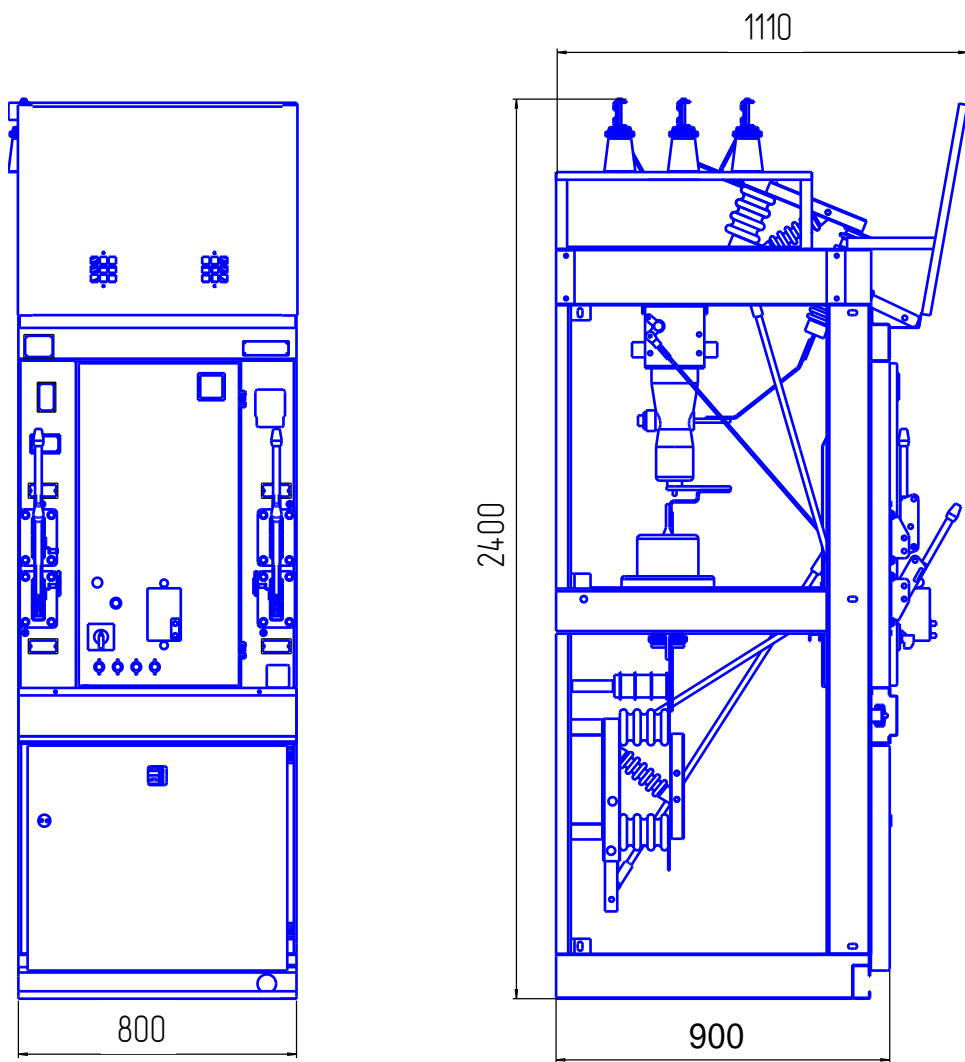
Габаритные размеры камеры КСО - 203 - 04
